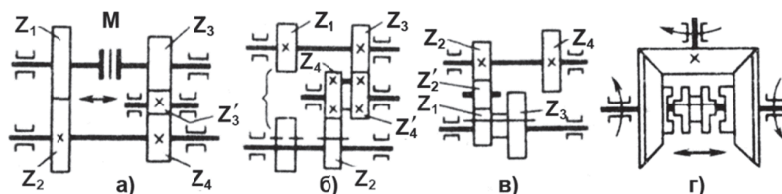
Кинематические схемы (а-г) реверсивных механизмов
